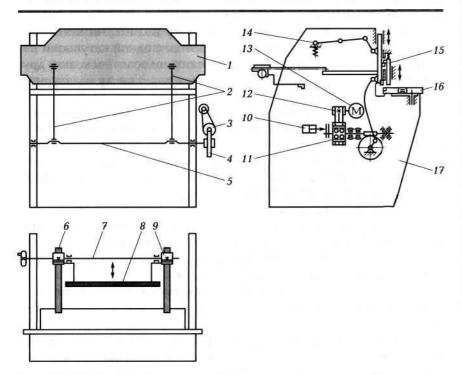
Кинематическая схема кривошипных листовых ножниц
